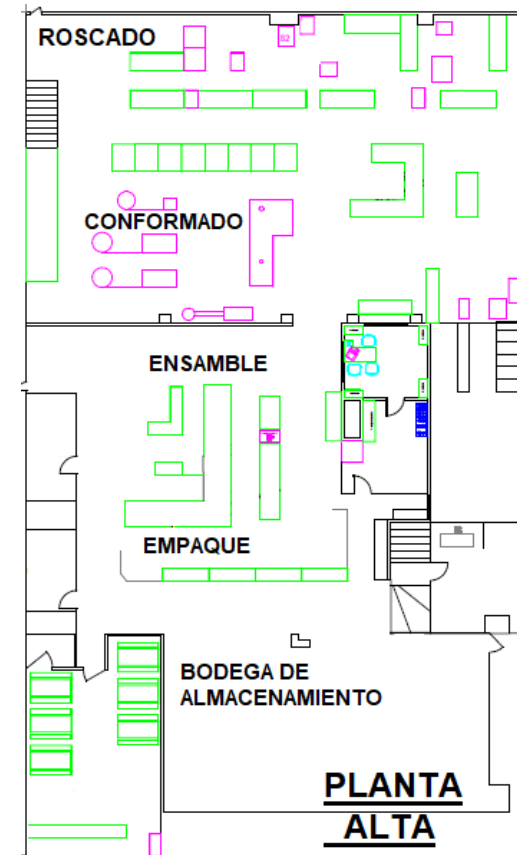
LAYOUT planta alta producción BPH. (Fuente: La empresa)
